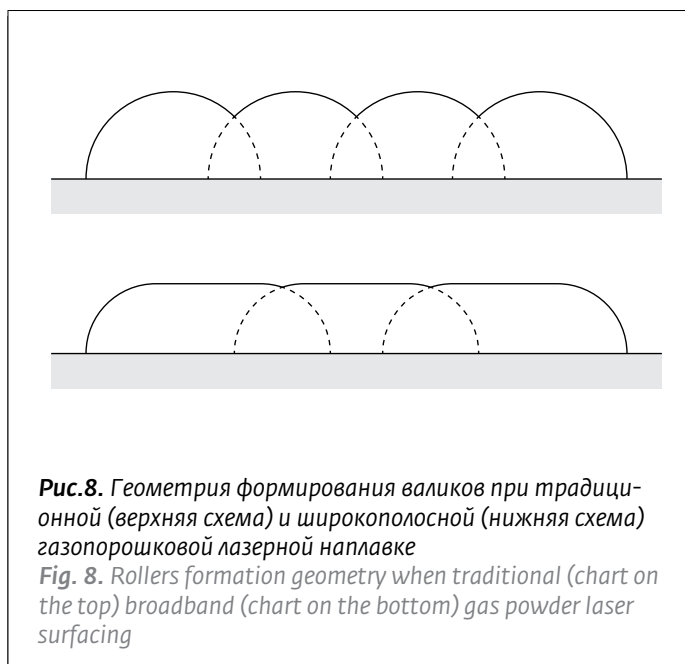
Геометрия формирования валиков при традиционной (верхняя схема) и широкополосной (нижняя схема) газопорошковой лазерной наплавке
